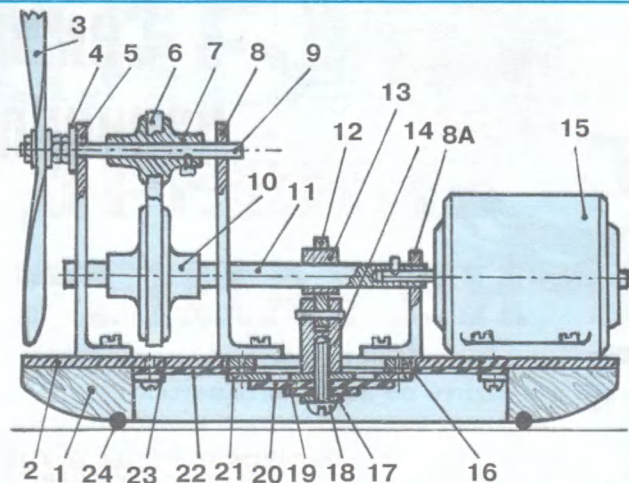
Устройство и размещение деталей: 1 — нижняя часть корпуса; 2 — верхняя несущая пластина; 3 — воздушный винт; 4 — фторопластовая шайба; 5, 8, 8А — стойки; 6 — пассик; 7 — ведомый шкив; 9 — ось винта; 10 — ведущий шкив; 11 — ведущий вал; 12 — шток; 13 — эксцентрик-кулачок; 14 — центральный шарнир диффузора; 15 — электродвигатель; 16 — центральное кольцо; 17, 18 — винт с шайбой; 19 — резиновая шайба; 20 — клапанная «ромашка»; 21 — центральная клапанная часть; 22 — мембрана (резина); 23 — большое кольцо; 24 — резиновый жгут.
